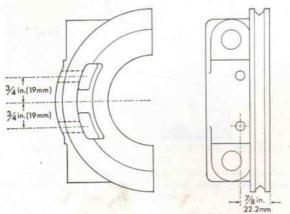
TROUS DE RETOUR D'HUILE DANS LE CHAPEAU ARRIERE
